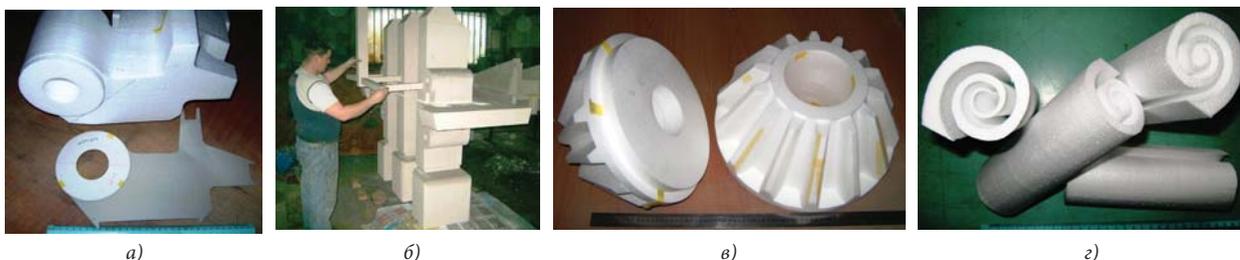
Примеры изготовления моделей вырезанием проволокой: а) торец модели и картонный шаблон, б) модель детали МНЛЗ (машины непрерывного литья заготовок) для формовки способом Full Mould – в песчаной смеси со связующим, в) конические шестерни, г) витые модели деталей крана.
